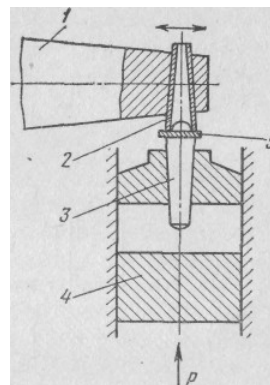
Ультразвуковая сварка по контуру:
